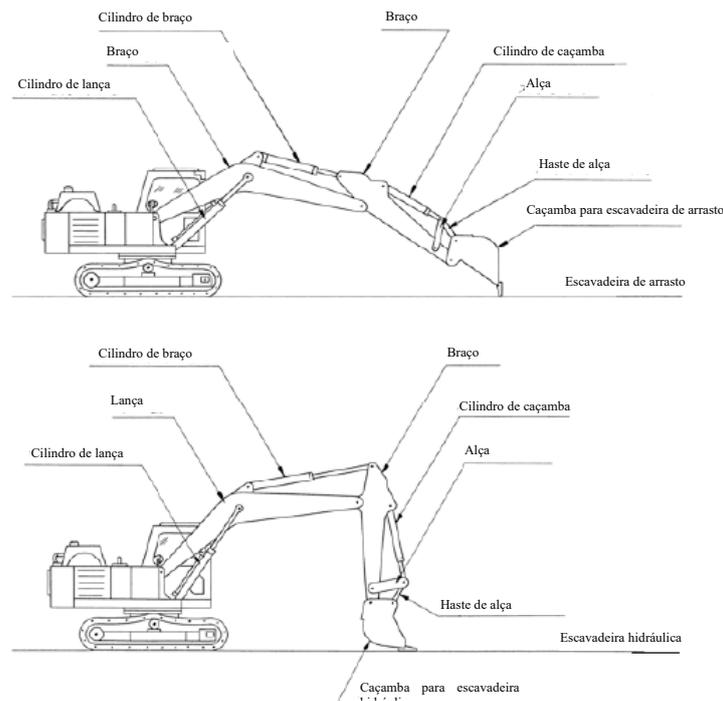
Exemplo de equipamento de trabalho para escavadeiras hidráulicas
